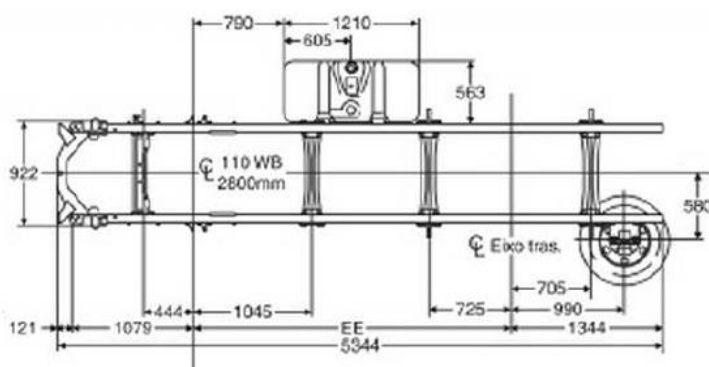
Desenho técnico linha Cargo C-815, Implementador (2011)
